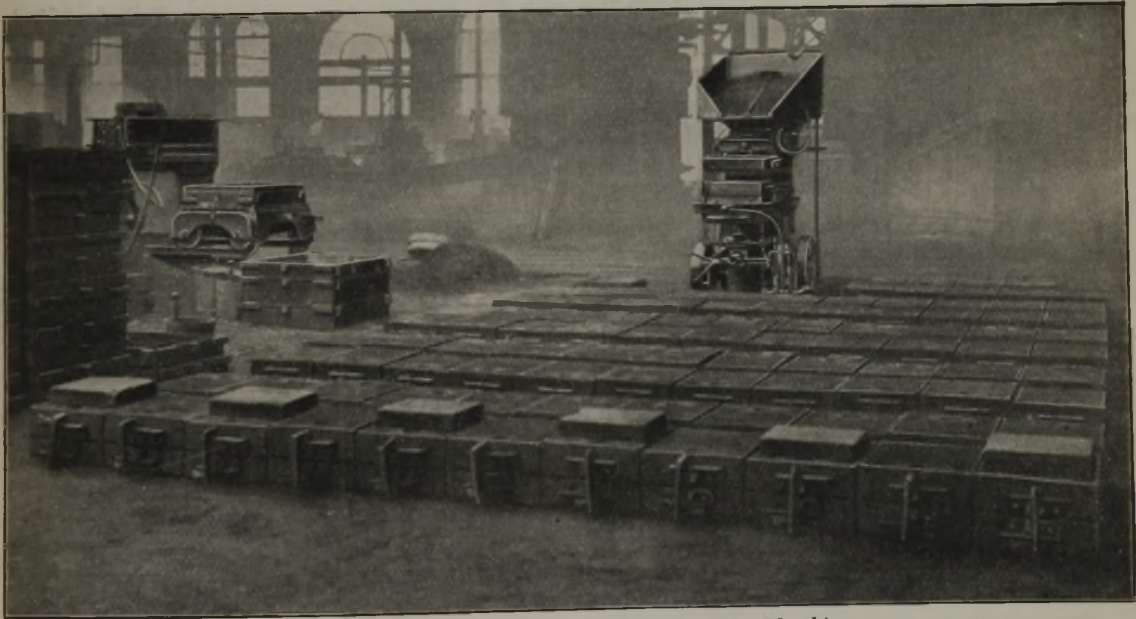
Achtstündiges Ausbringen einer Maschine.
